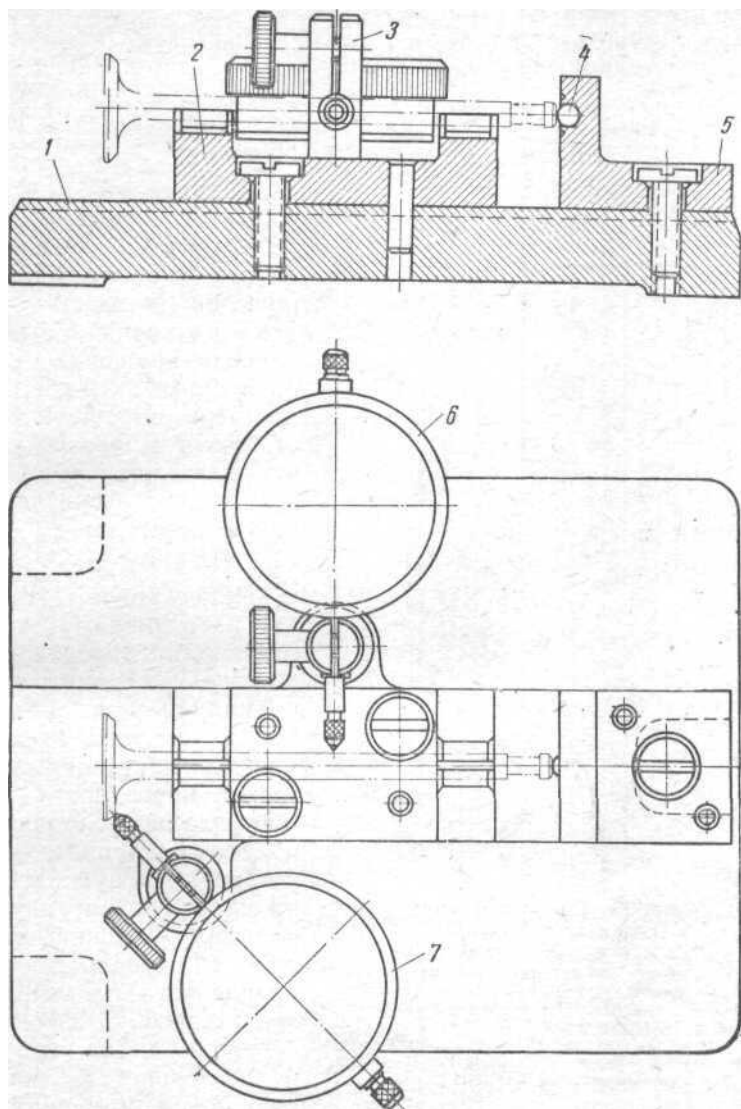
Проверка концентричности рабочей поверхности головки клапана относительно стержня
